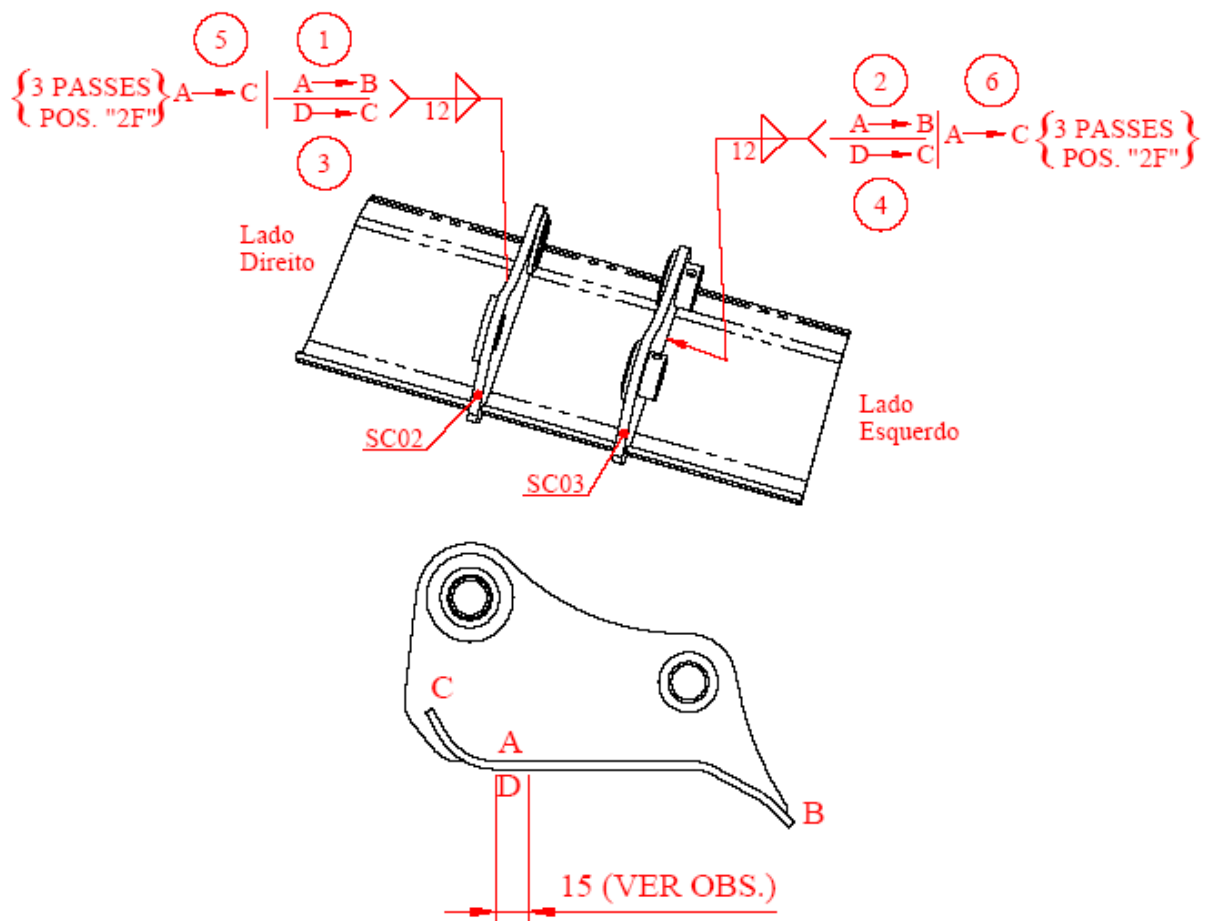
Seqüência de soldagem do Subconjunto SC04
